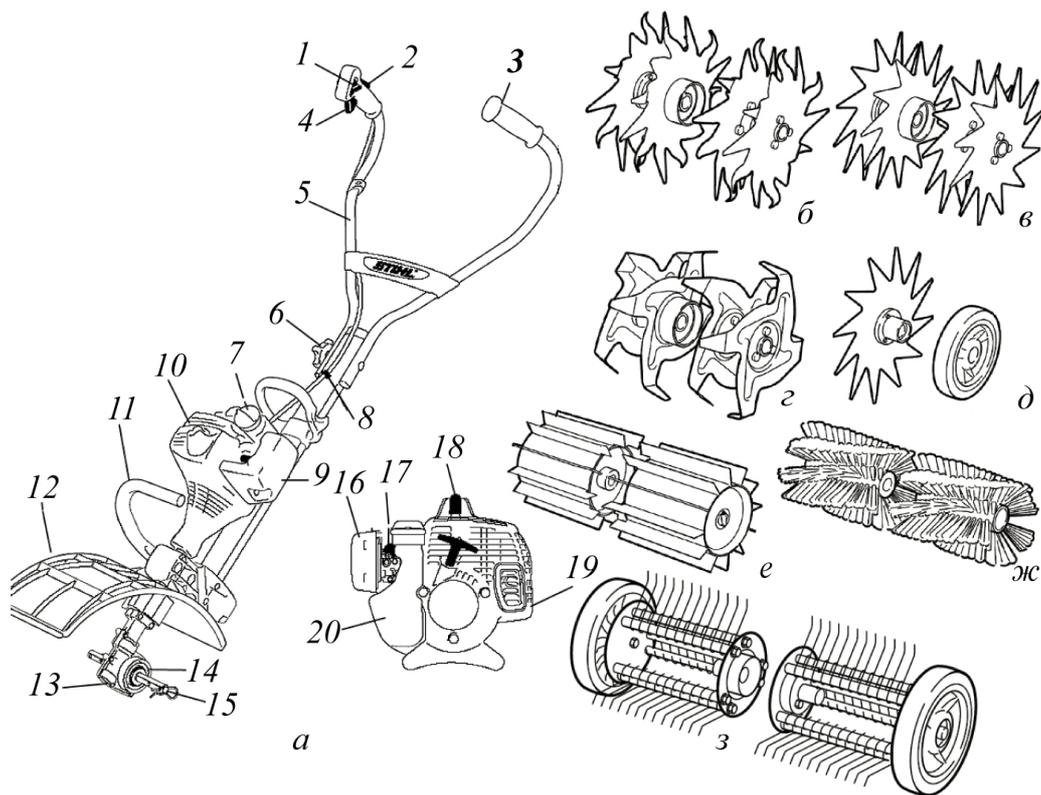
Мультифункциональная система «Stihl MM55»: 1 – органы управления; 2 – блокировка газа; 3 – ручка; 4 – регулятор газа; 5 – рукоятки; 6 – винт регулировки рукояток; 7 – крышка топливного фильтра; 8 – держатели; 9 – воздушный фильтр; 10 – двигатель; 11 – рука для перноски; 12 – защитный щиток; 13 – редуктор; 14 – вал; 15 – стопор; 16 – карбюратор; 17 – топливный насос; 18 – свеча; 19 – глушитель; 20 – топливный бак
